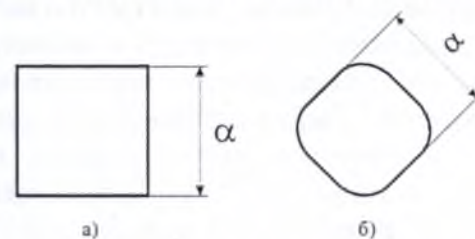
Процесс формирования при центробежной абразивной обработке: а) исходная заготовка – куб со сторонами a ; б) заготовка после операции галтовки
